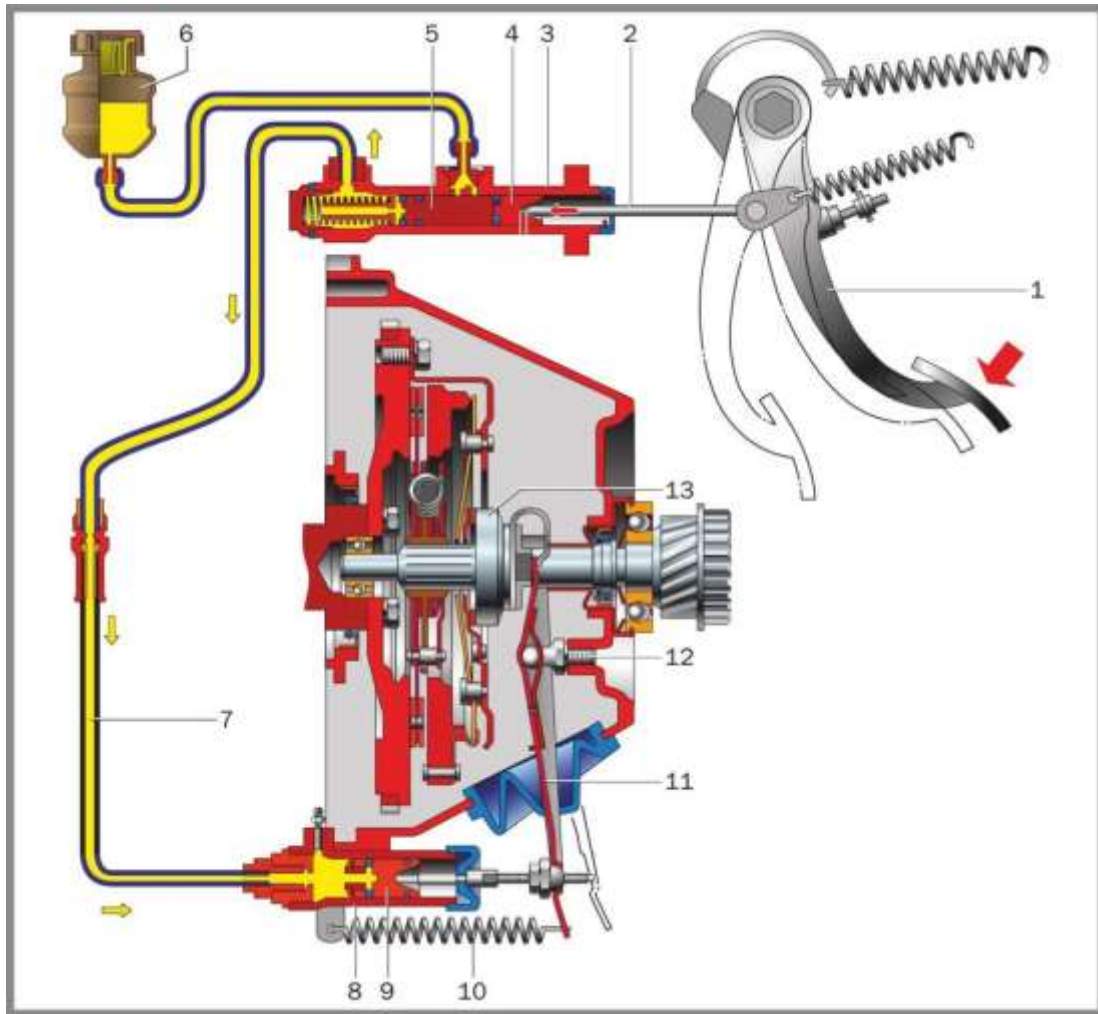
Схема гiдрравлічного приводу зчеплення: 1 – педаль; 2 – штовхач; 3 – головний циліндр; 4 – поршень штовхача; 5 – поршень головного циліндра; 6 – бачок; 7 – трубопровід; 8 – робочий циліндр; 9 – поршень; 10 – пружина; 11 – вилка; 12 – опора вилки; 13 – вижимний підшипник
